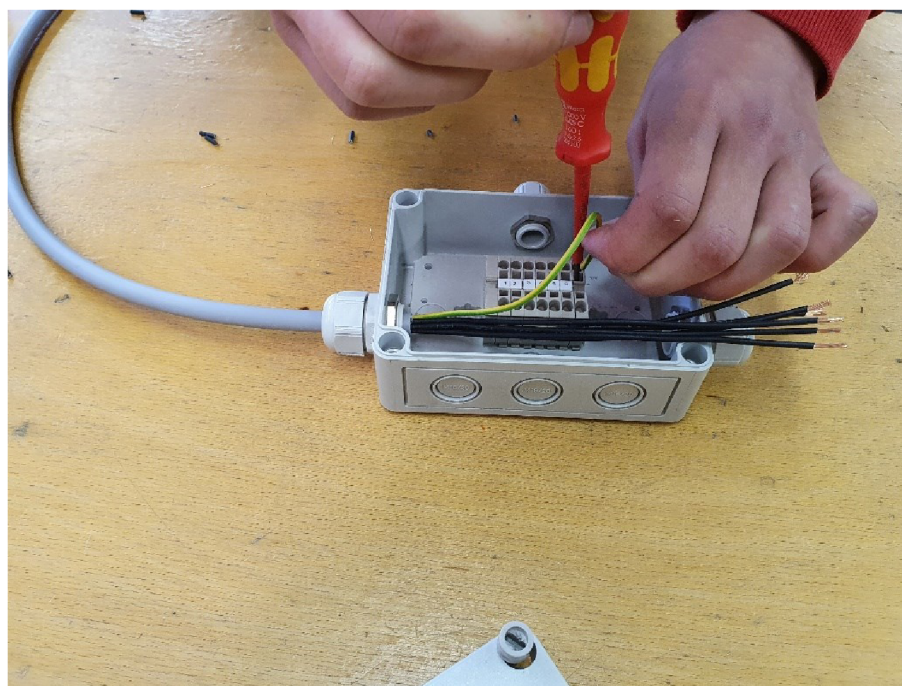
Žáci ve výrobním procesu v oblasti elektrotechniky. Foto autor.
